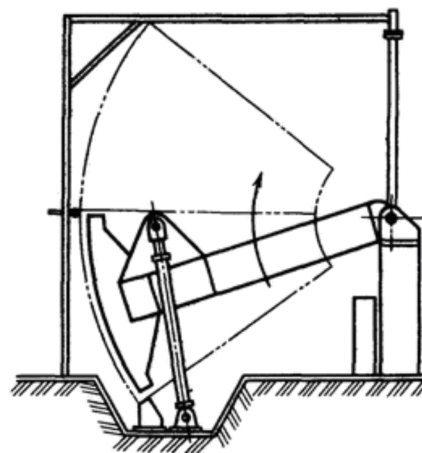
Стенд для электрошлаковой сварки или дуговой сварки с принудительным формированием шва
